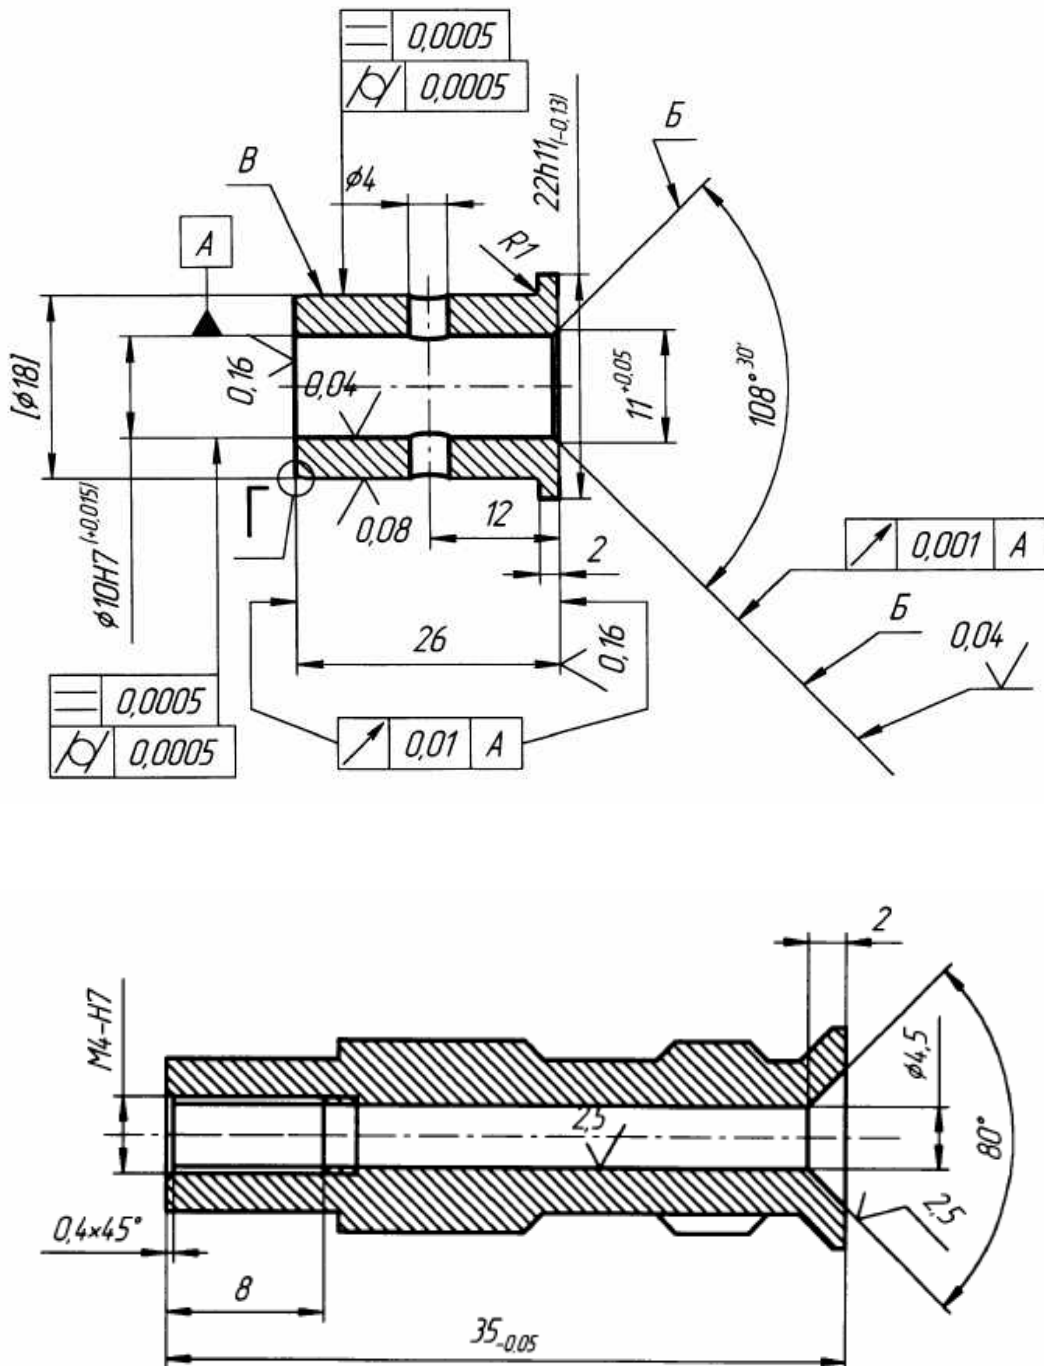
Креслення втулки та електрокерованого клапана
